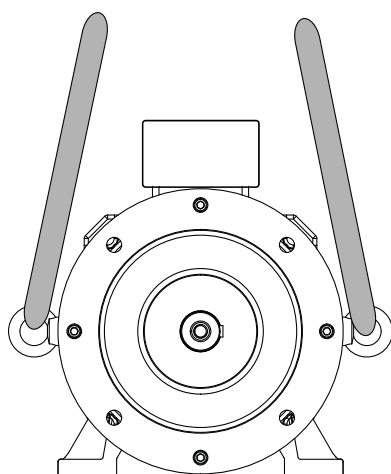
Trasporto del motore con due asole di sollevamento a lato del corpo motore
